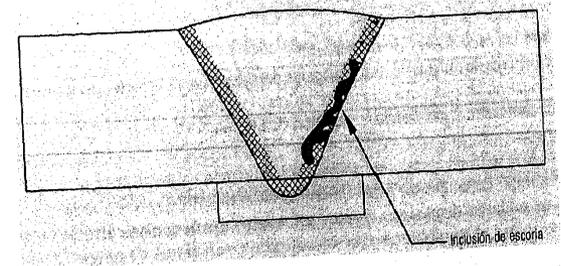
Inclusión de escoria en una soldadura.
